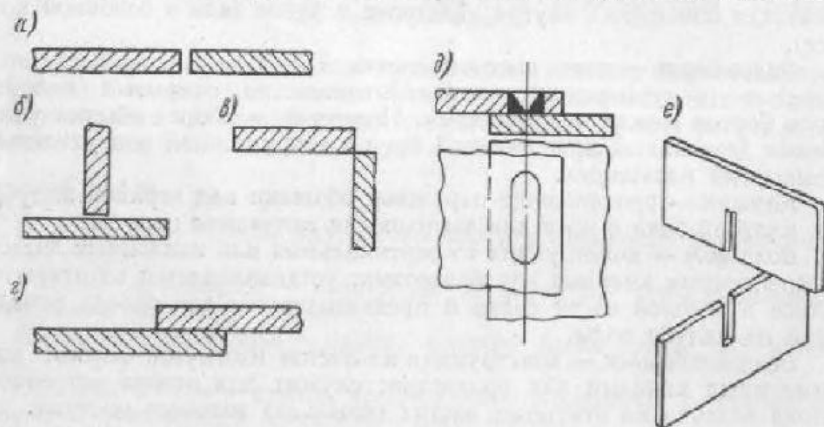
Типы сварных соединений: а — соединение встык; б — тавровое; в — угловое; г — внакрой; д — прорезное; е — гребенчатое.
